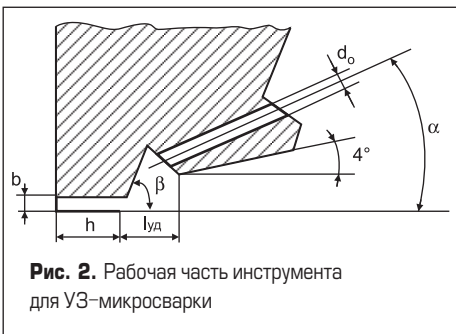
Рабочая часть инструмента для УЗ-микросварки
